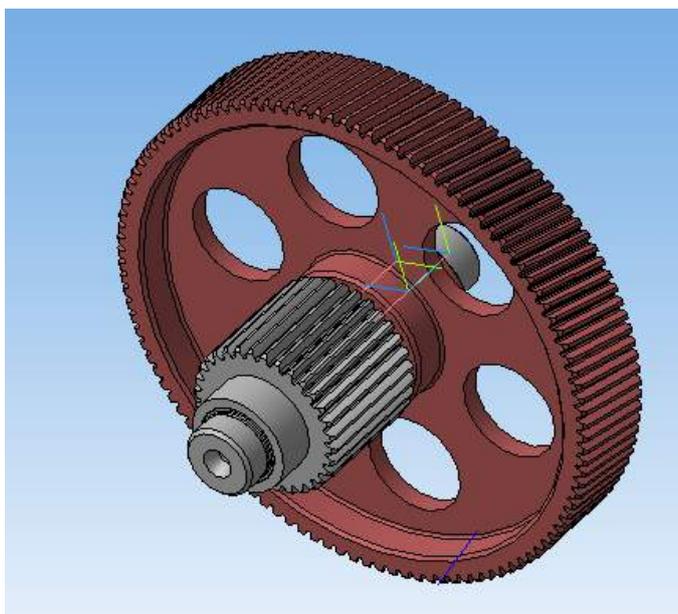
3D сборка промежуточной зубчатой передачи : вал-шестерня, колесо, шпонка (вид сзади)
